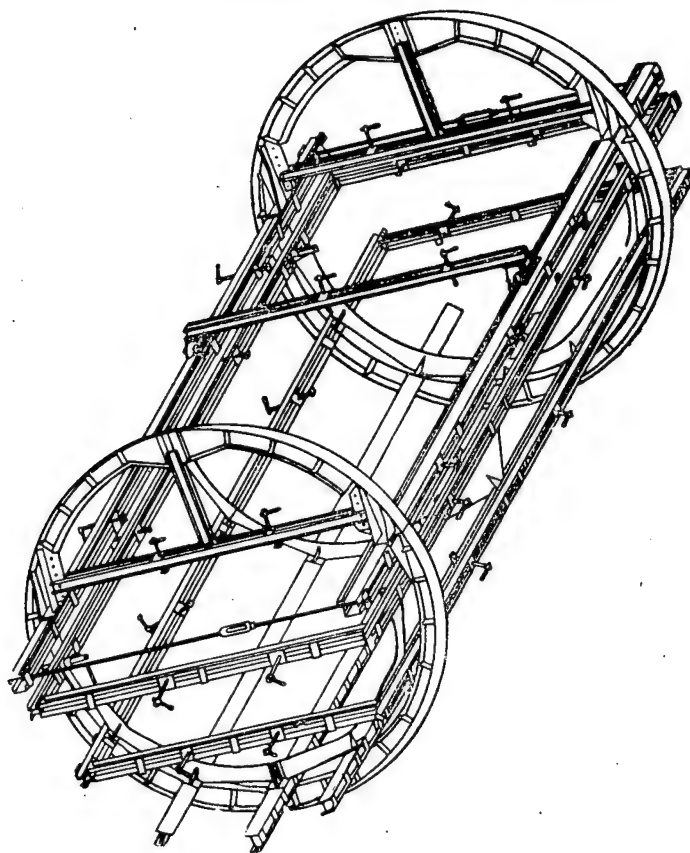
Кондуктор-кантователь для сборки и сварки блок-секций
